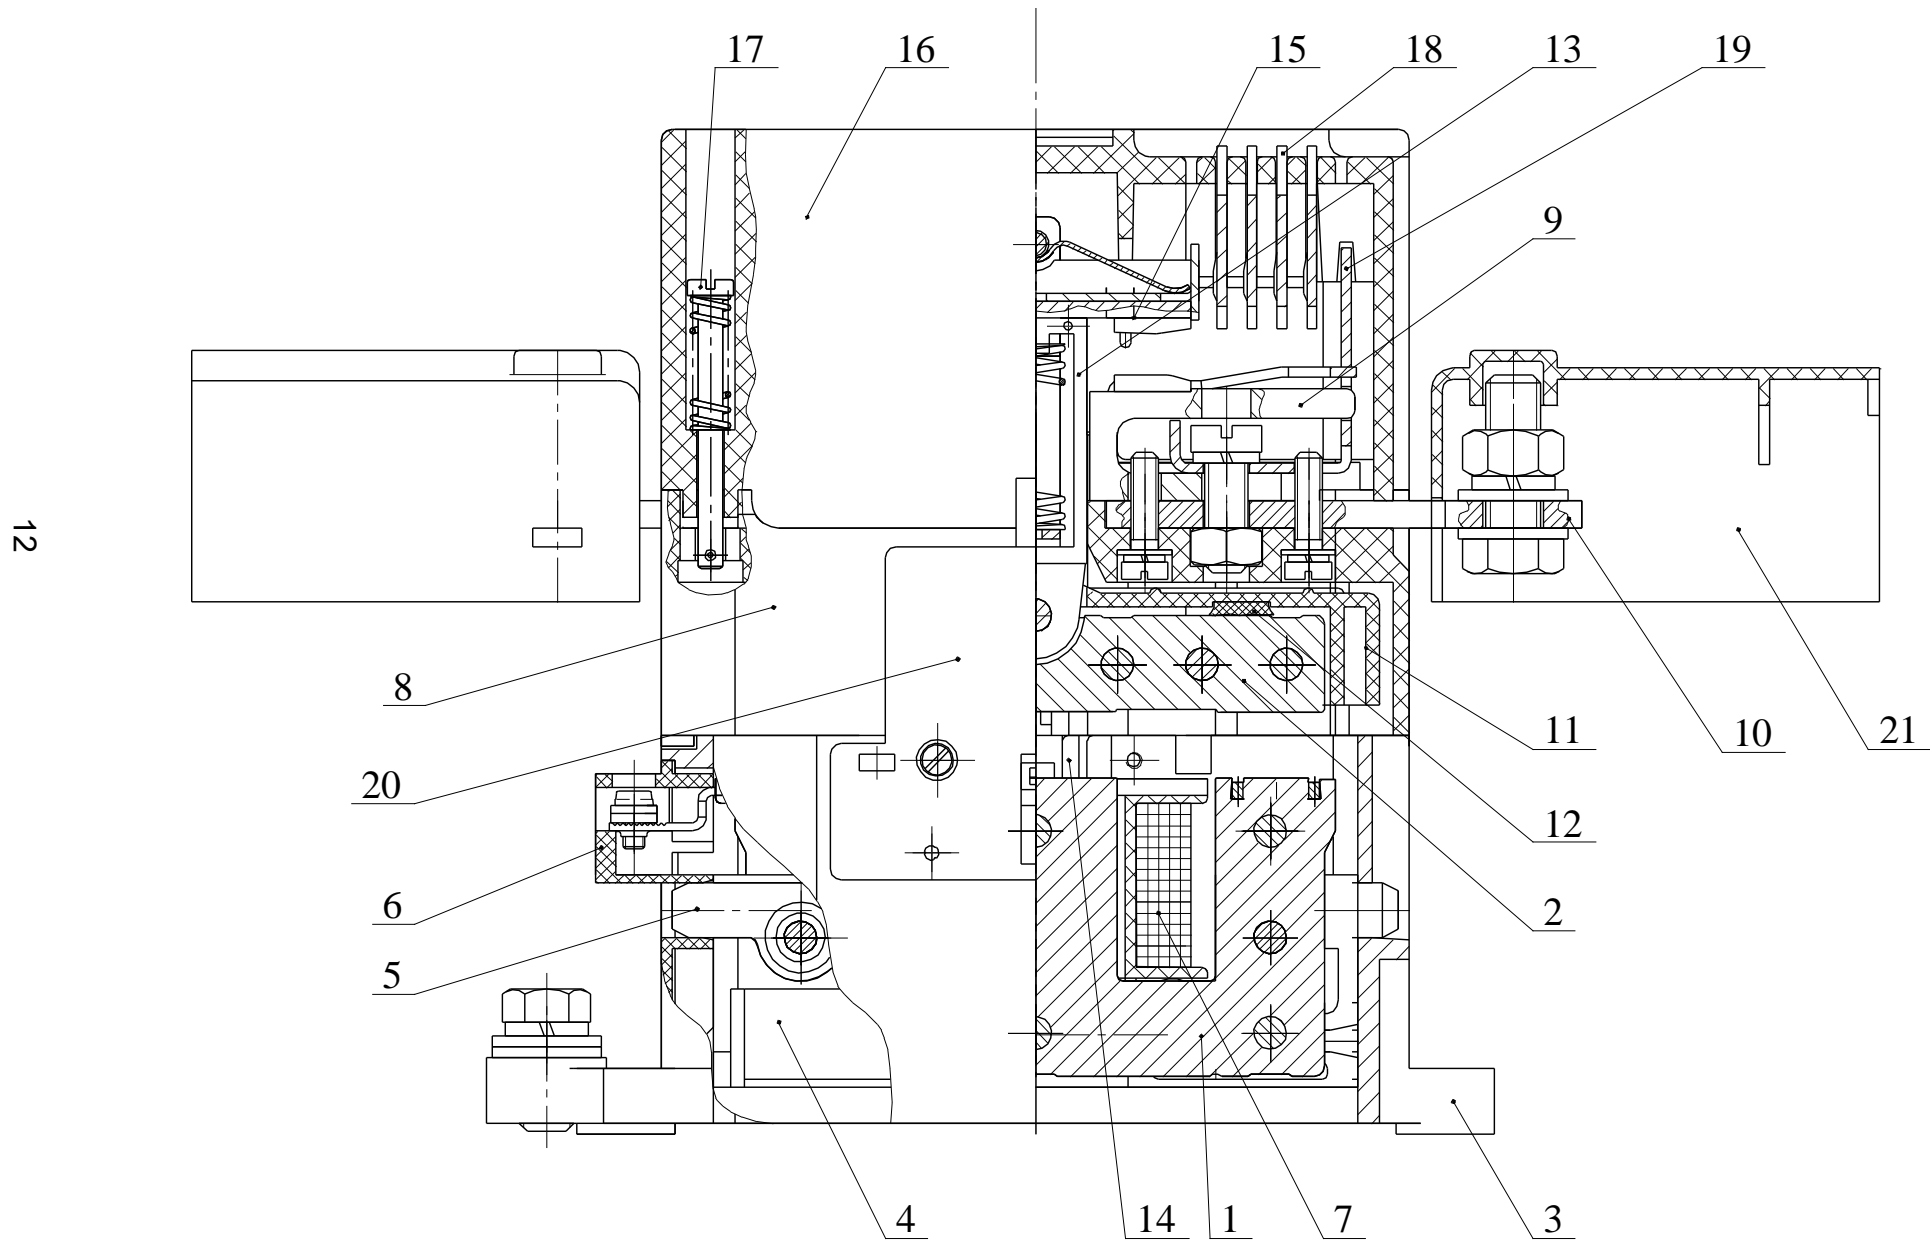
Контактор нереверсивный ПМЛ-7101, ПМЛ-7161
